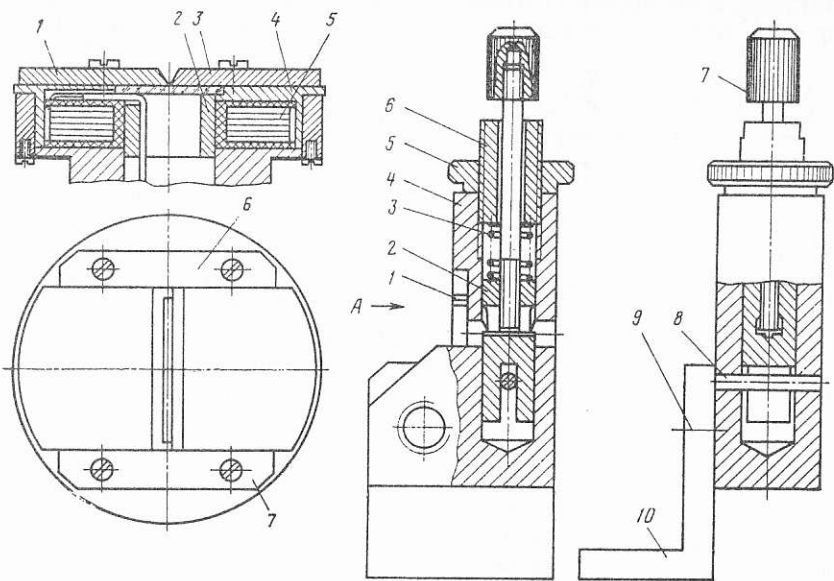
Приспособление для лазерной сварки проволочек и приварке проволочек к листовым деталям
